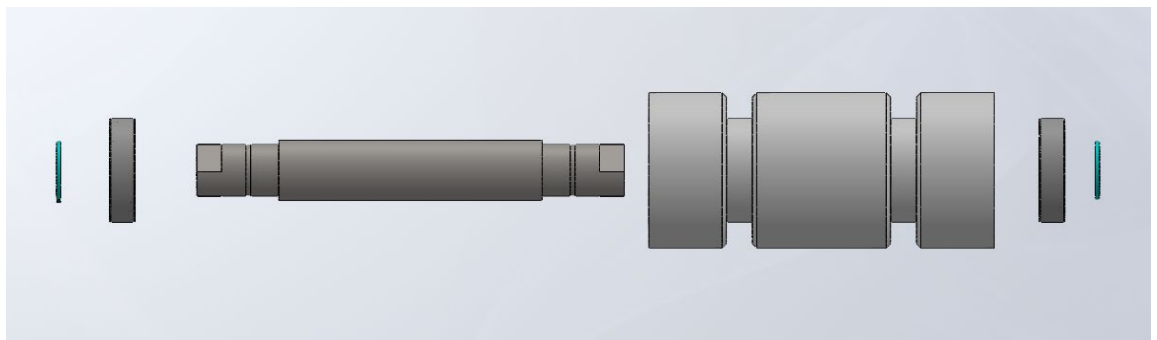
Натяжний ролик конвеєра, подетальний вид
